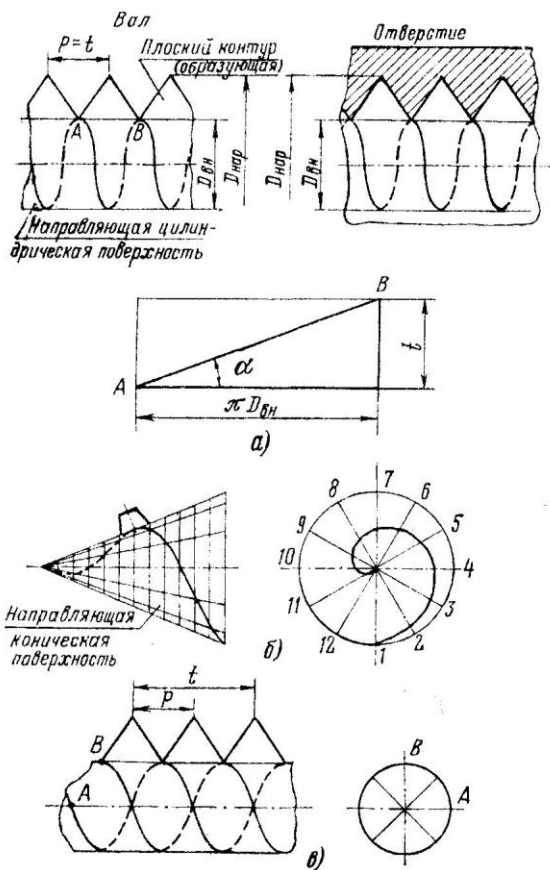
Образование резьбовой поверхности: а — цилиндрической однозаходной; б — конической однозаходной; в — цилиндрической многозаходной
